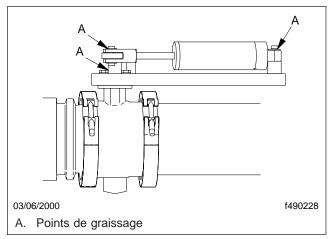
, Frein sur échappement et cylindre pneumatique Pacbrake
